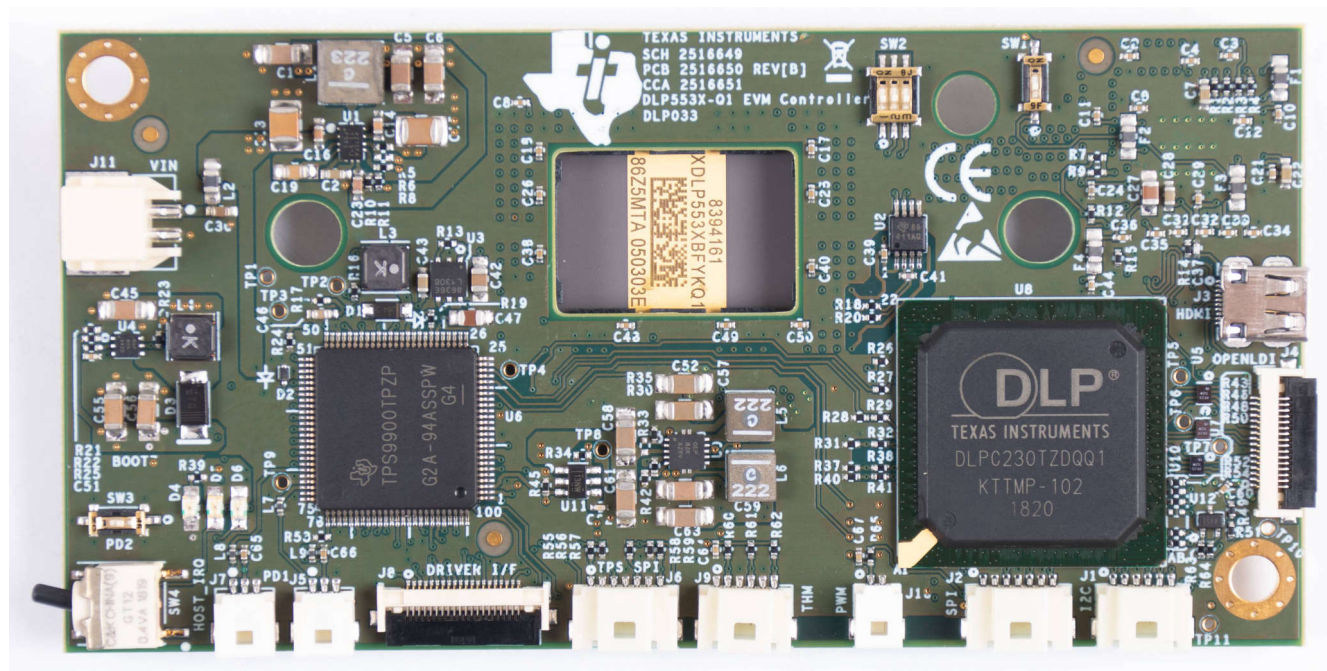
DLP5530PROJTGQ1EVM コントローラ PCB
